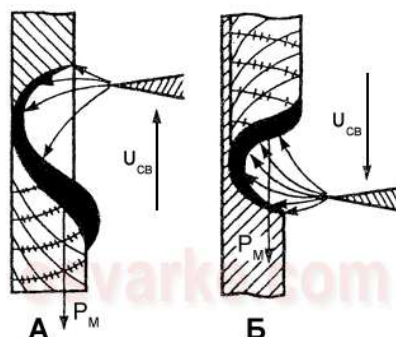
Ручная дуговая сварка швов в вертикальном положении
